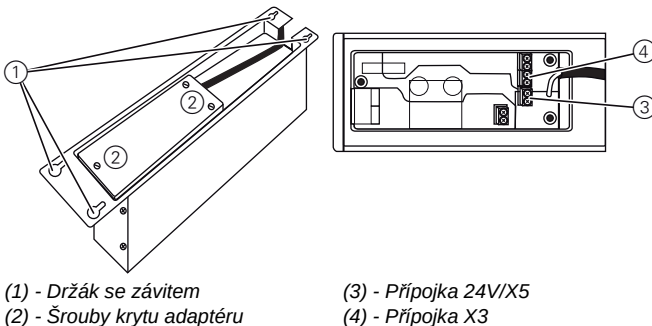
Montáž transformátoru osvětlení šicího stroje
